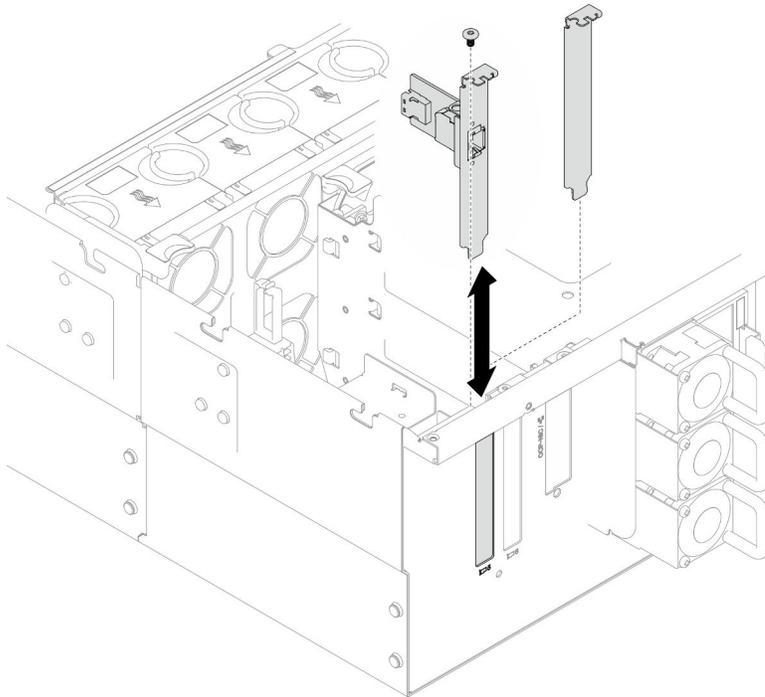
Entfernen der Ethernet-Anschlussbaugruppe
